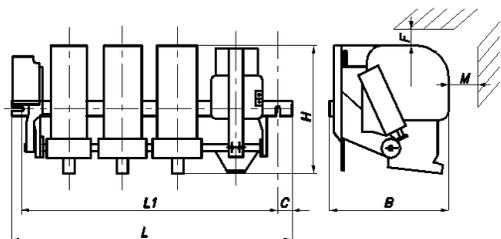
Общий вид и габаритные размеры КТ-5000.
